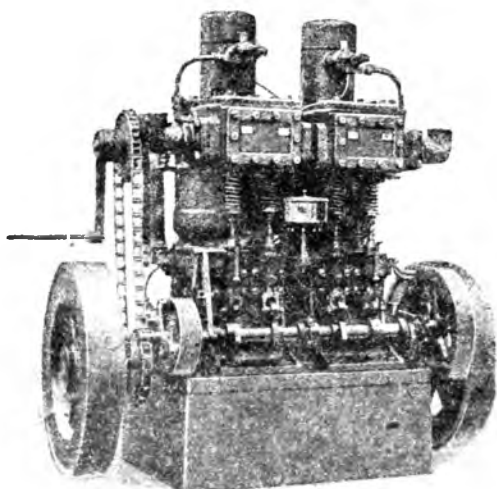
Рукоятка для пуска въ ходъ двухцилиндроваго лодочнаго двигателя тяжелаго-типа, помѣщенная на добавочной оси у верхней части цилиндровъ. Ось на подставкѣ, привинченной къ основанію цилиндровъ. Вращеніе передается цѣпью. Отношеніе зубчатокъ таково, что вращеніе нѣсколько облегчается. Двигатель *Dan* въ 20 лш. силъ.
